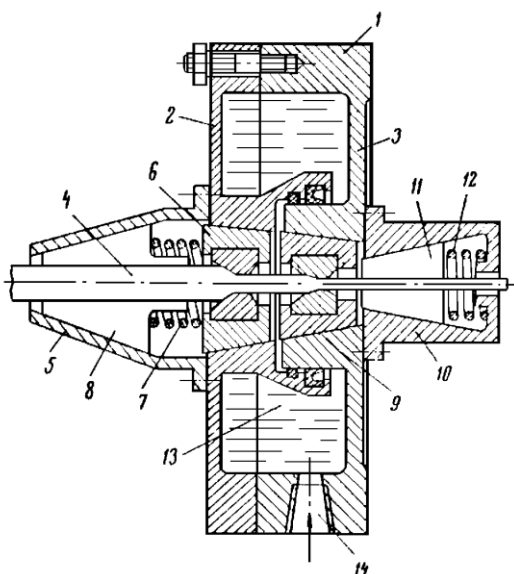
Устройство для деформирования металла волочением и вдавливанием
